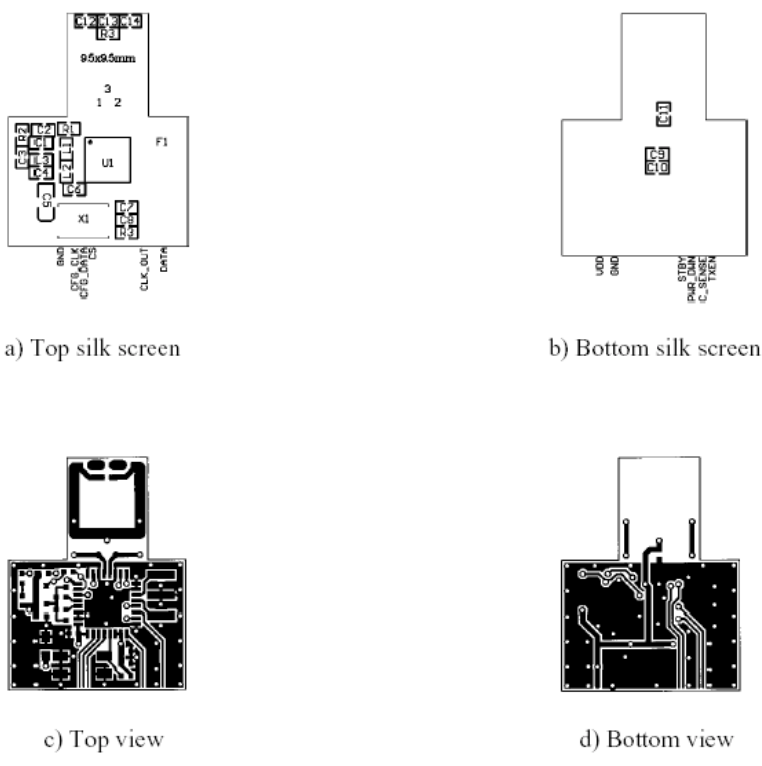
nRF903 环形天线的 PCB 布局 (868MHz)
